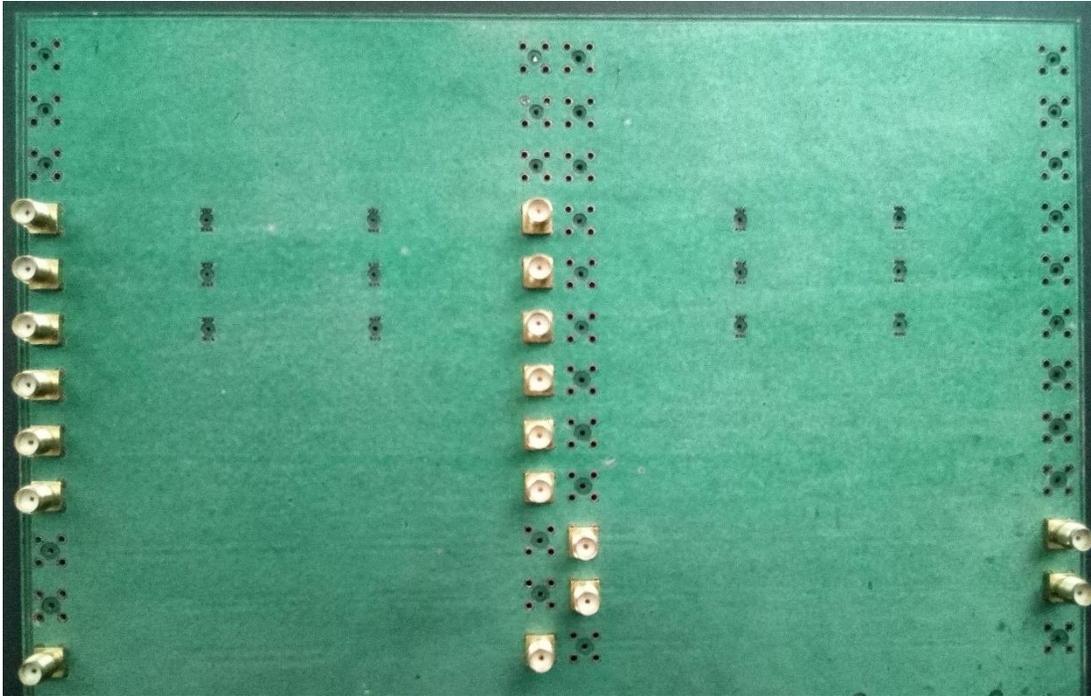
Acabado final del PCB cuatro capas, vista bottom
